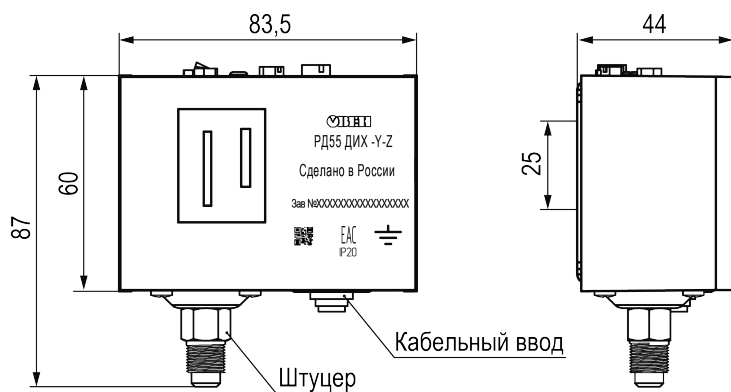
Габаритные и присоединительные размеры прибора
